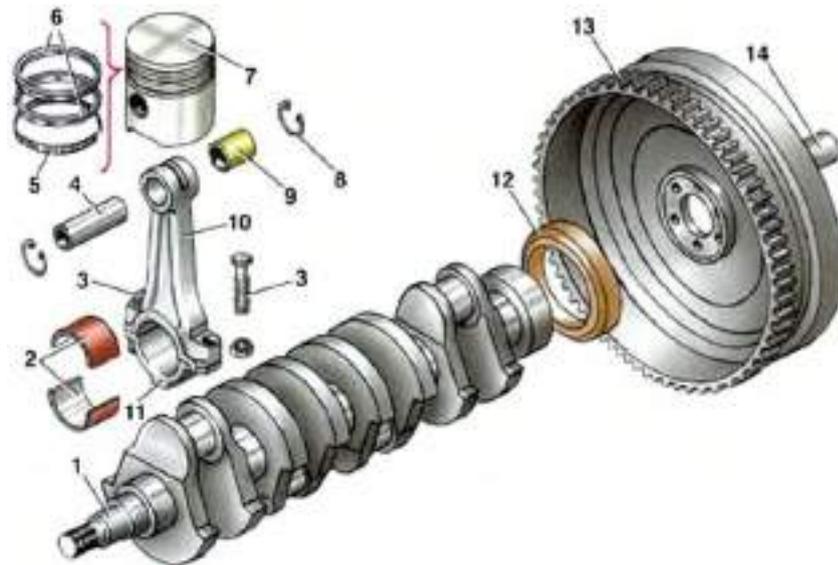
Детали кривошипно-шатунного механизма: 1 – коленчатый вал; 2 – вкладыш шатунного подшипника; 3 – шатунный болт; 4 – палец; 5 – маслосъемное кольцо; 6 – компрессионное кольцо; 7 – поршень; 8 – стопорное кольцо; 9 – втулка головки шатуна; 10 – шатун; 11 – крышка шатуна; 12 – задний сальник коленчатого вала; 13 – маховик; 14 – подшипник первичного вала коробки передач
